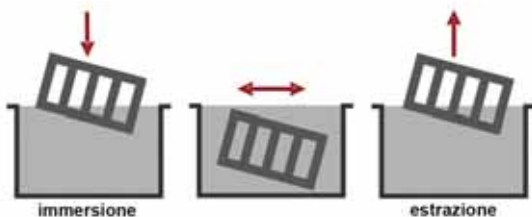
L'immersione e l'estrazione sono nella stessa direzione
